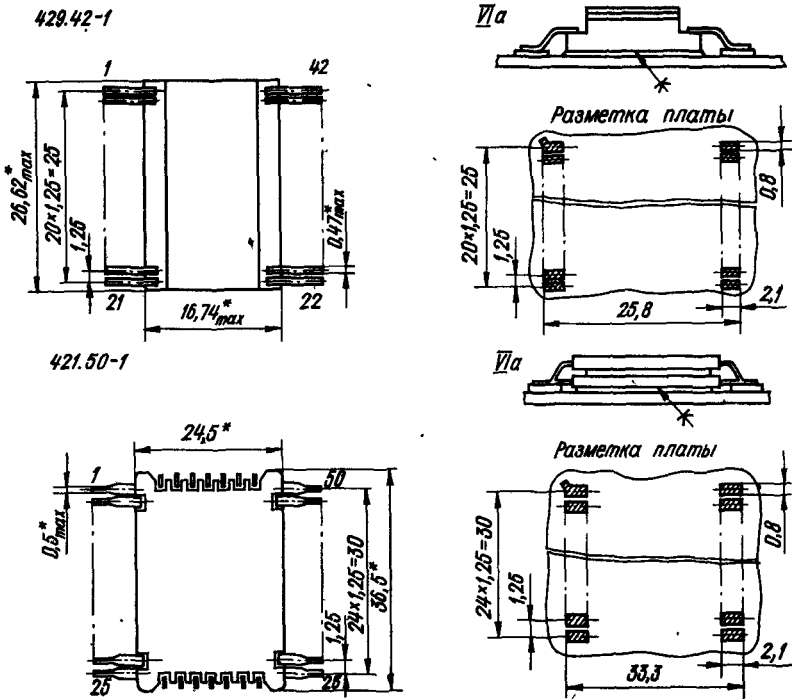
Габаритные и установочные размеры и варианты установки микросхем в корпусе типа 4 (✱ обозначены размеры для справок)
